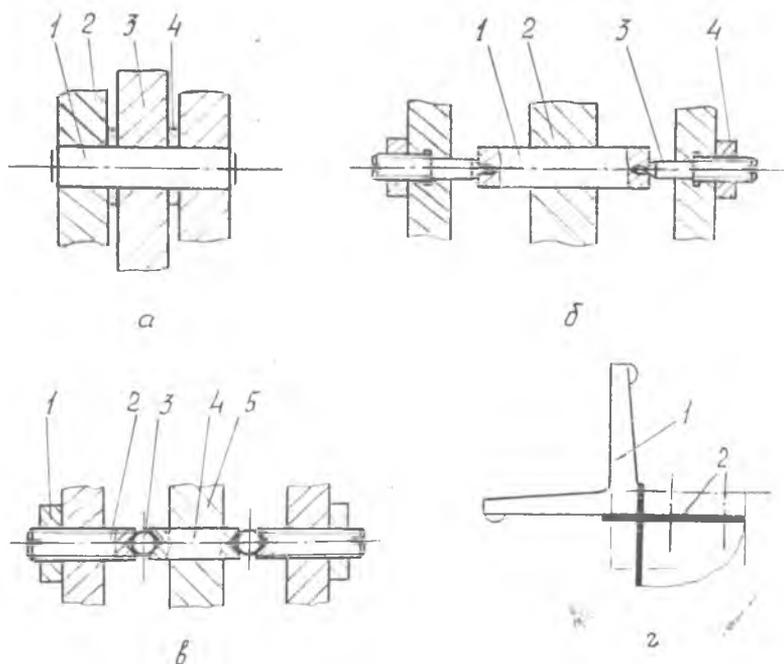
Конструкции рычагов, качающихся: а — на штифте (1 — штифт, 2 — корпус приспособления, 3 — рычаг, 4 — шайба регулировочная); б — на центрах (1 — ось, 2 — рычаг, 3 — центр, 4 — контргайка); в — в шариках (1 — контргайка, 2 — центр обратный, 3 — шарик, 4 — ось, 5 — рычаг); г — на плоских пружинах (1 — рычаг, 2 — пружина плоская)
